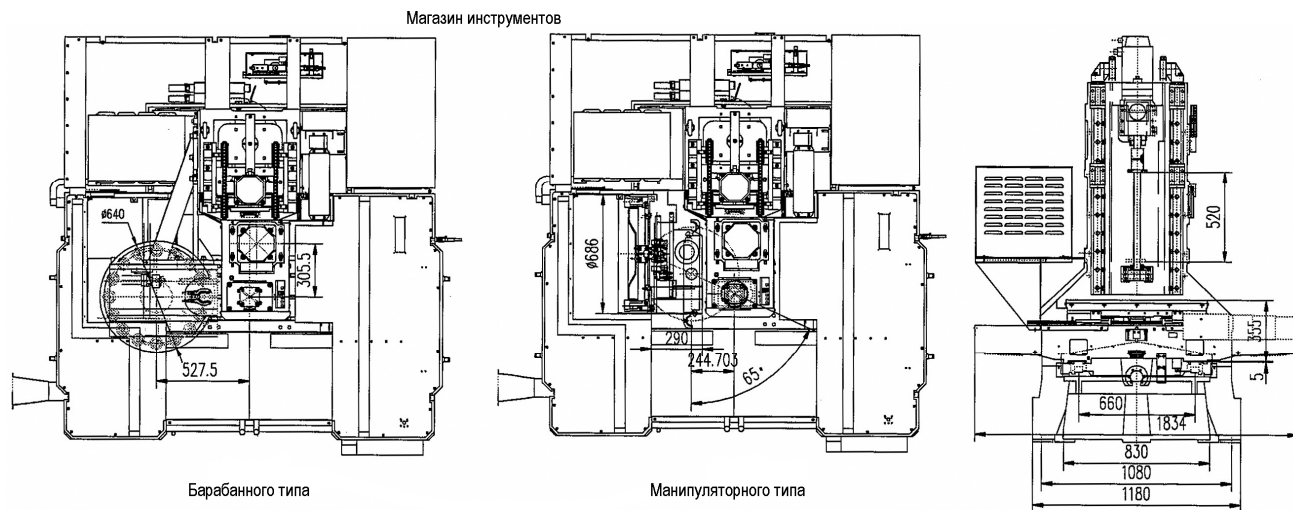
Расположение основных частей обрабатывающего центра VDL-800A
